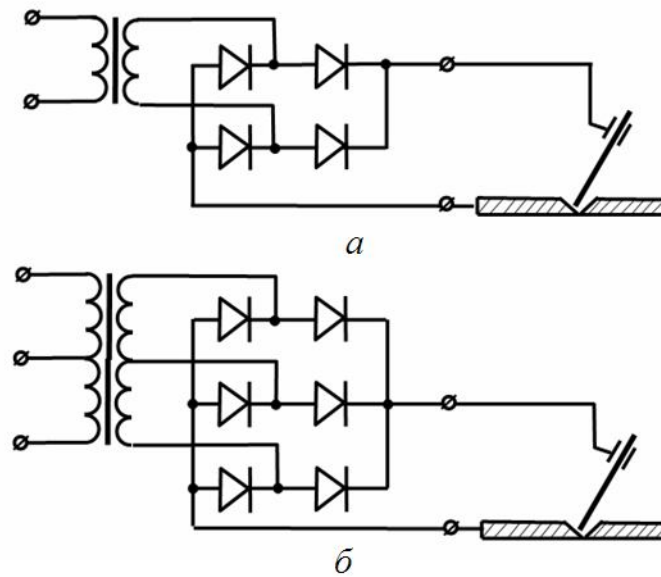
Схеми зварювальних випрямлячів:
